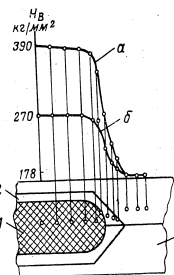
Твердость точечного сварного шва. Материал — сталь 12Г2А толщиной 2+2 мм.
